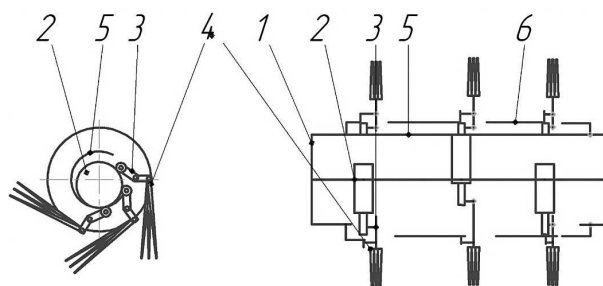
Схема вибратора: 1 – вал; 2 – кулачок; 3 – рычаг; 4 – палец; 5 – труба защитная; 6 – кожух
